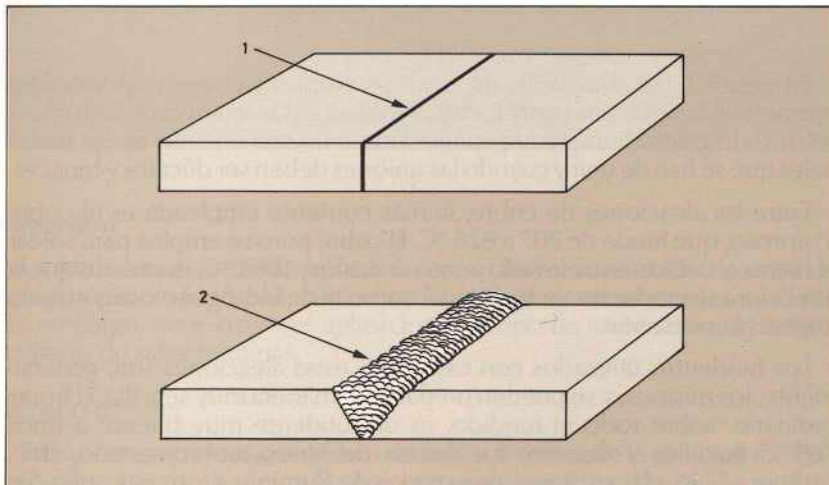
Unión mediante soldadura dura comparada con la soldadura por fusión: 1) soldadura dura; 2) cordón de soldadura por fusión.
